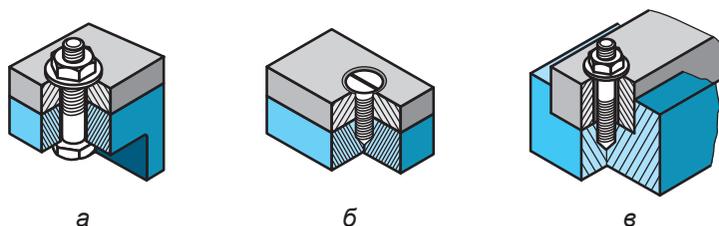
Виды резьбовых соединений: а – болтовое; б – винтовое; в – шпильное
